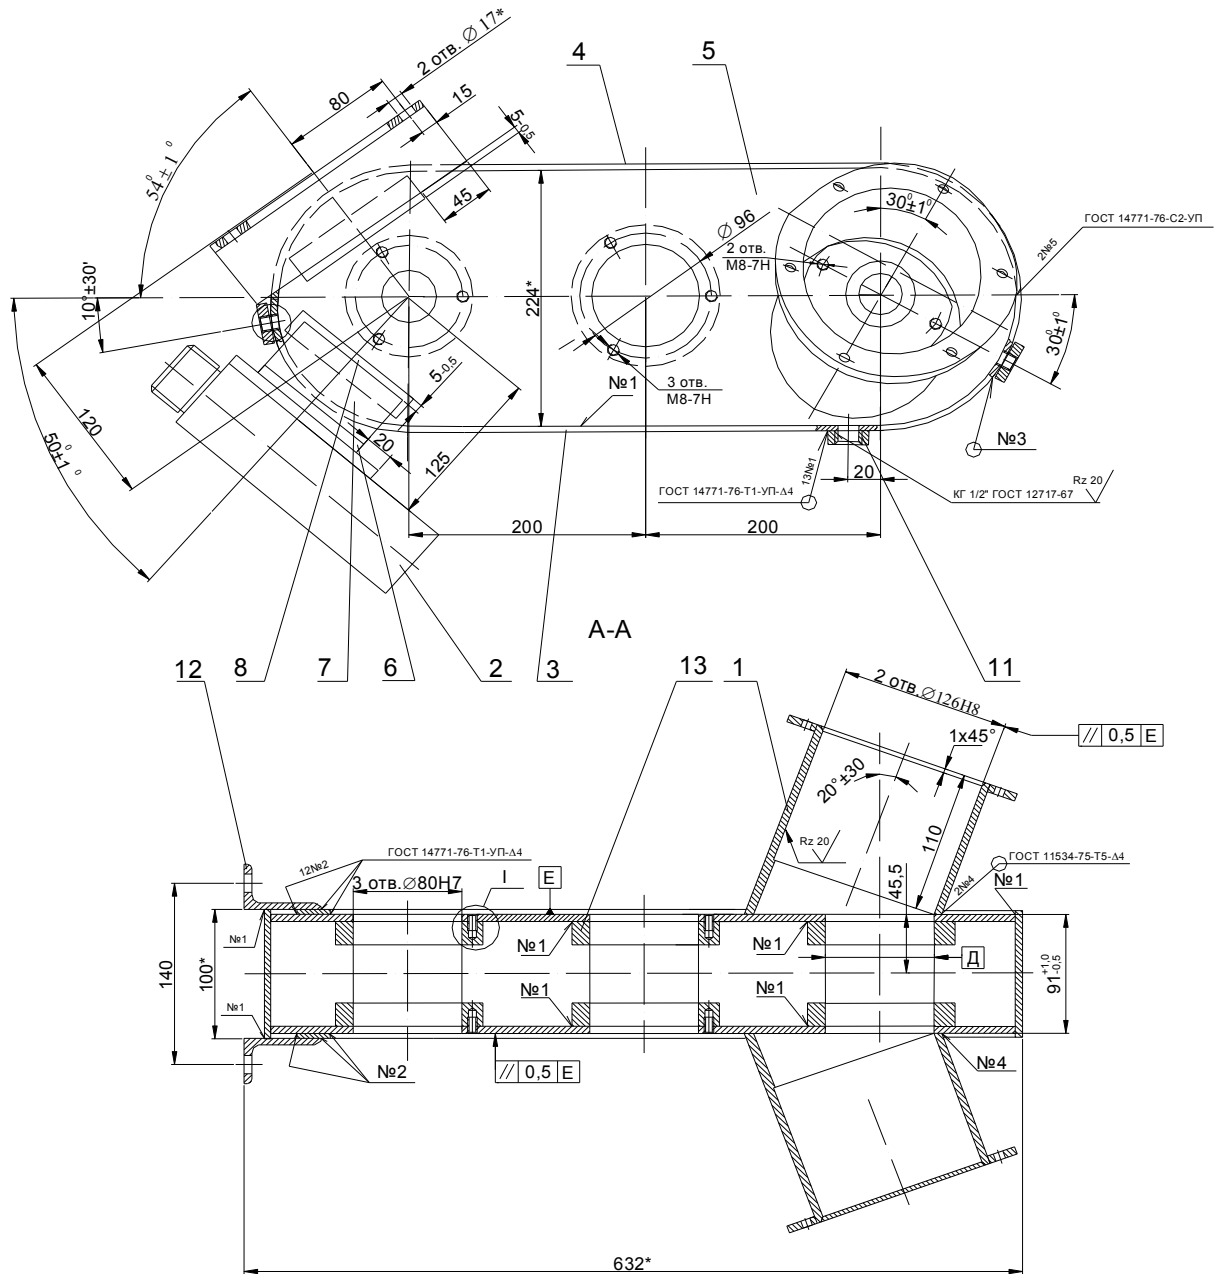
Базовий варіант корпусу редуктора
